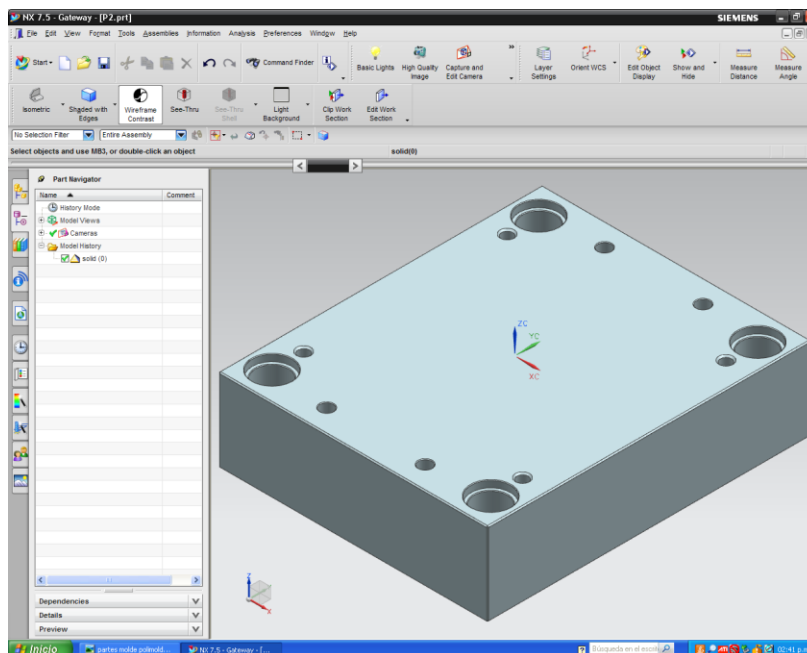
Placa posterior de cavidad P2, vista isométrica.
